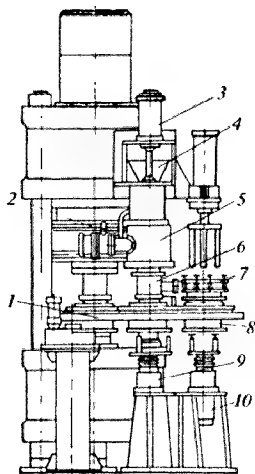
Формовочный агрегат с поворотным столом и задувной машиной: 1 — поворотный стол; 2 — разгрузочный клапан; 3 — шибер; 4 — бункер; 5 — задувная машина; 6 — приставка; 7 — пневмосъемник; 8 — пресс-форма; 9 — гидроцилиндр прижима; 10 — выталкиватель
